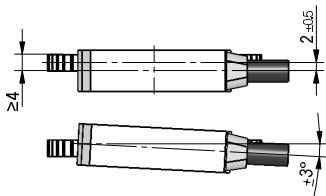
Definition der Zählrichtung mit Zahnrad und Montage Sensor, Abstandsmaße, Toleranzen
